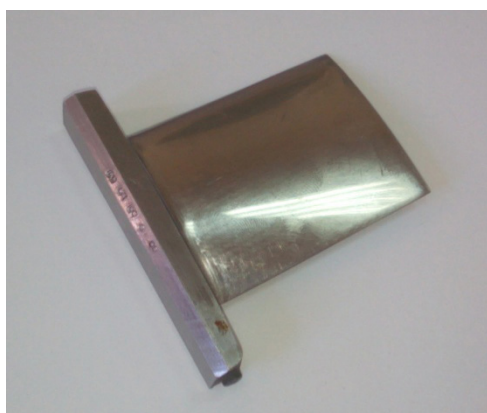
Лопатка 12-й ступени компрессора: ГТД
